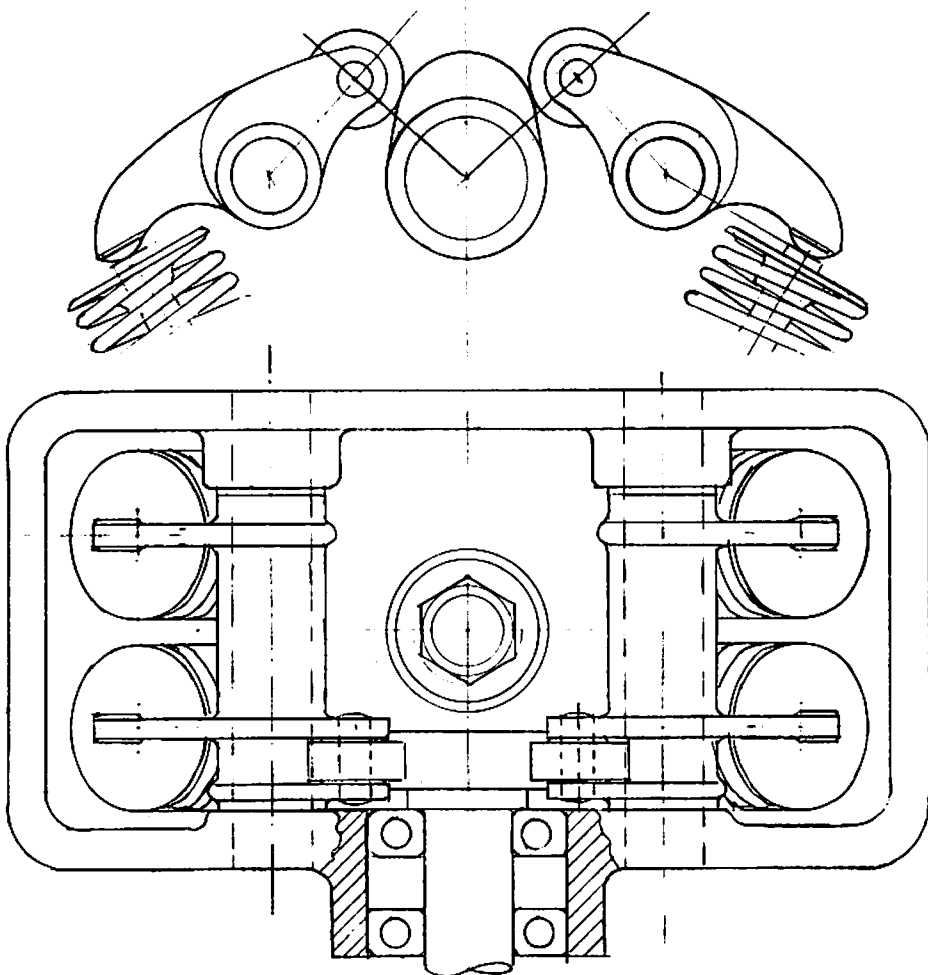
Ausgeführter Vierzylinderkopf des Verfassers mit einem Nocken pro Zylinder.
